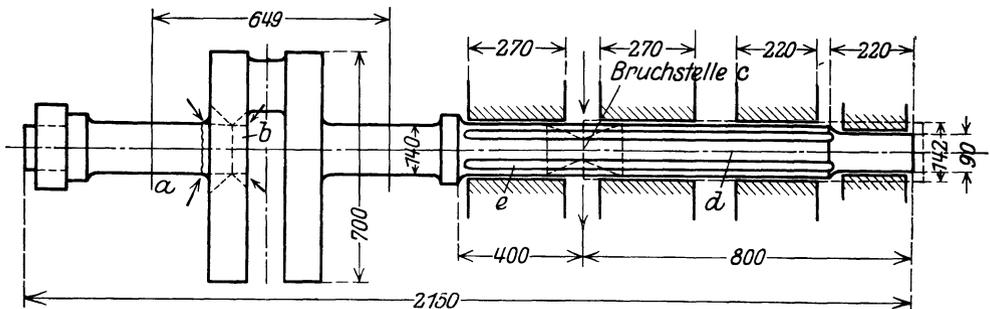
Schweißung von Kurbelwellenbrüchen.
